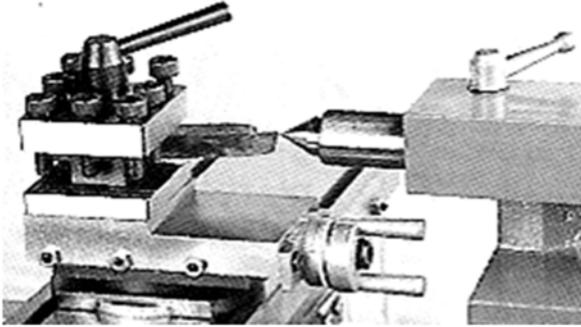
Einrichten der Bearbeitungswerkzeuge
